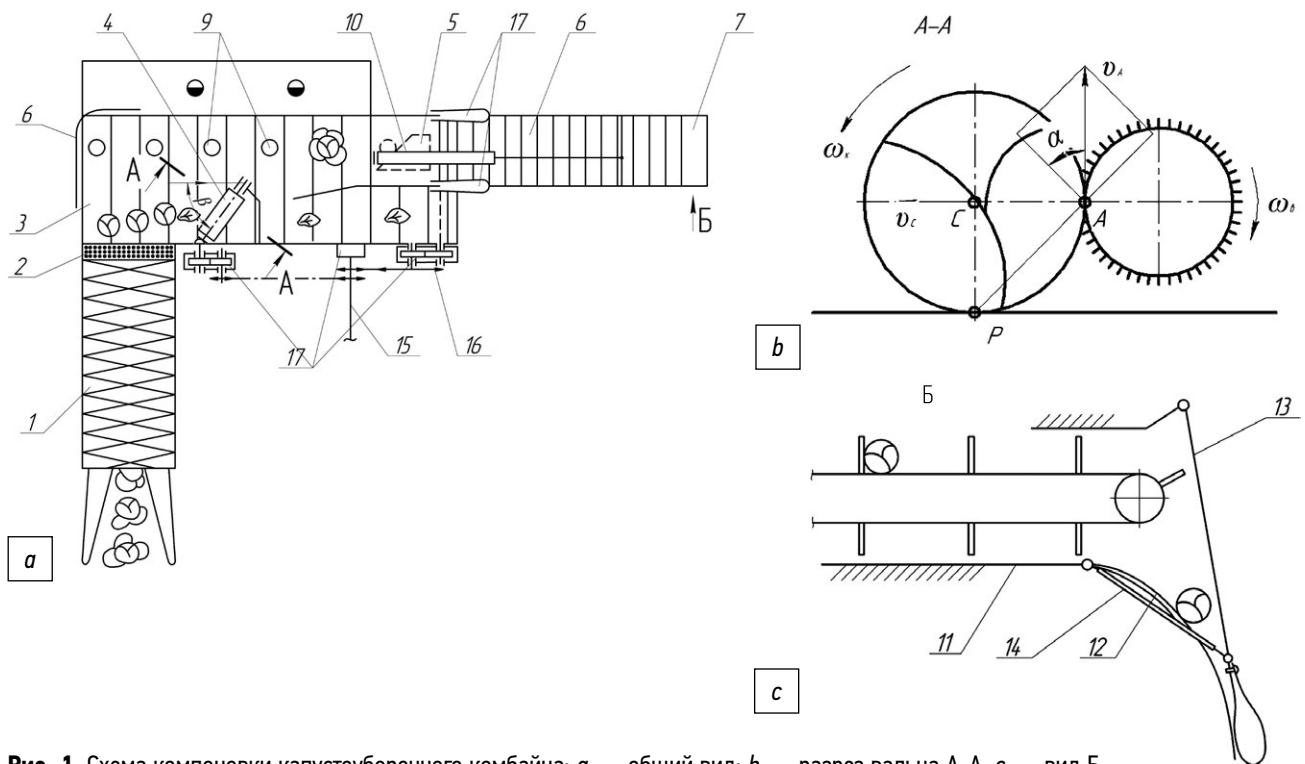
Схема компоновки капустоуборочного комбайна: *a* — общий вид; *b* — разрез вальца А-А, *c* — вид Б.
